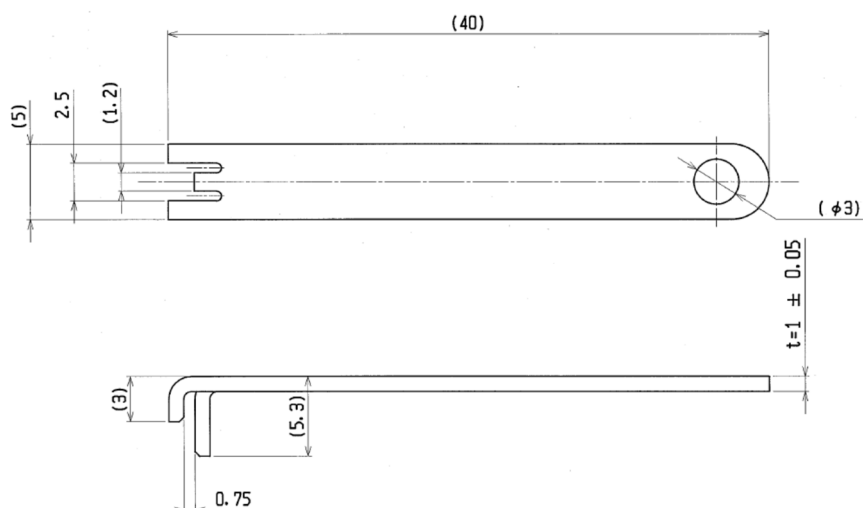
推奨 挿入抜去 JIG ※P/N: 90224-001
